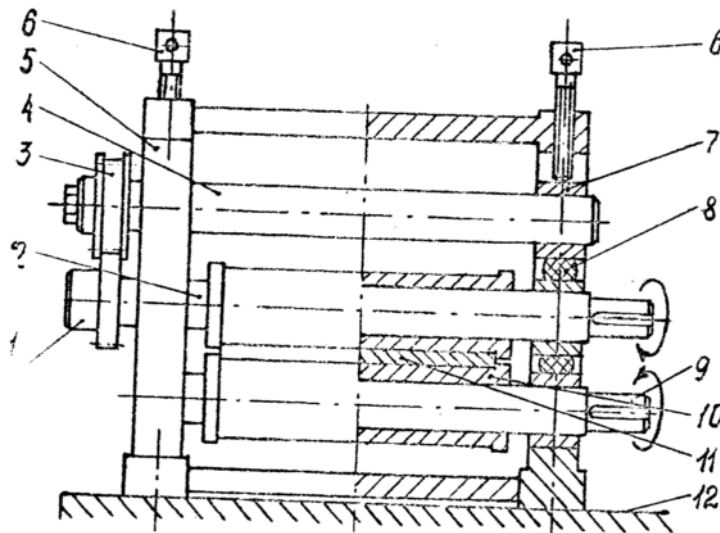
Схема и общий вид устройства для чистовой горячей накатки зубьев втулок
